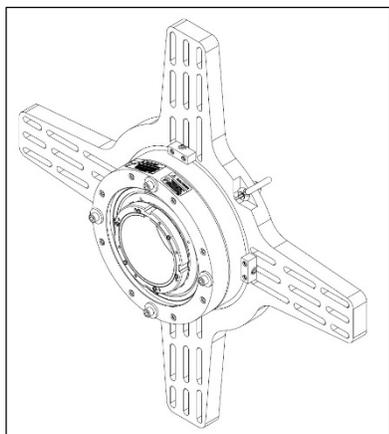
Самовыравнивающийся концевой узел с крестовиной
